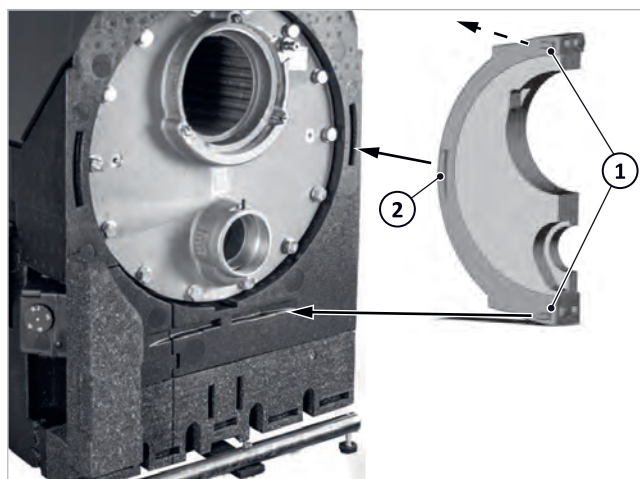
Isolamento anteriore della flangia (a destra, vista posteriore) con le molle di arresto
